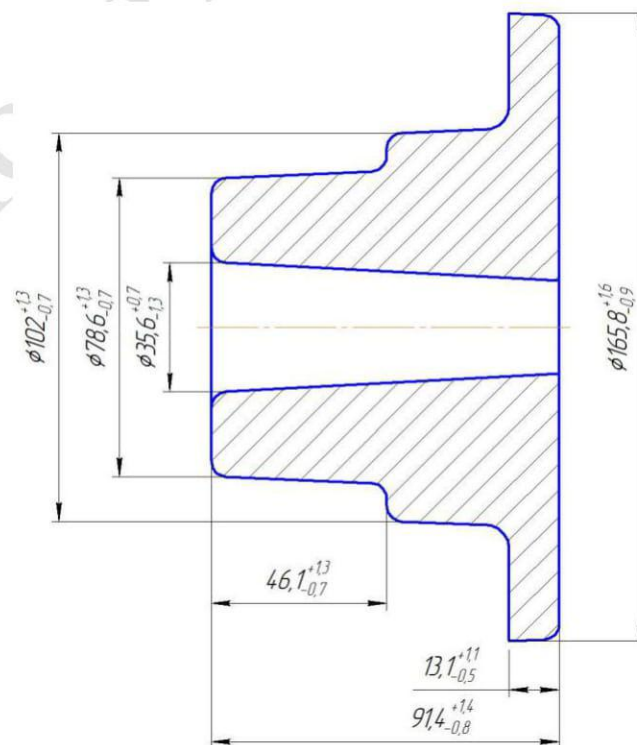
Виготовлення заготовки штампуванням на КГШП
